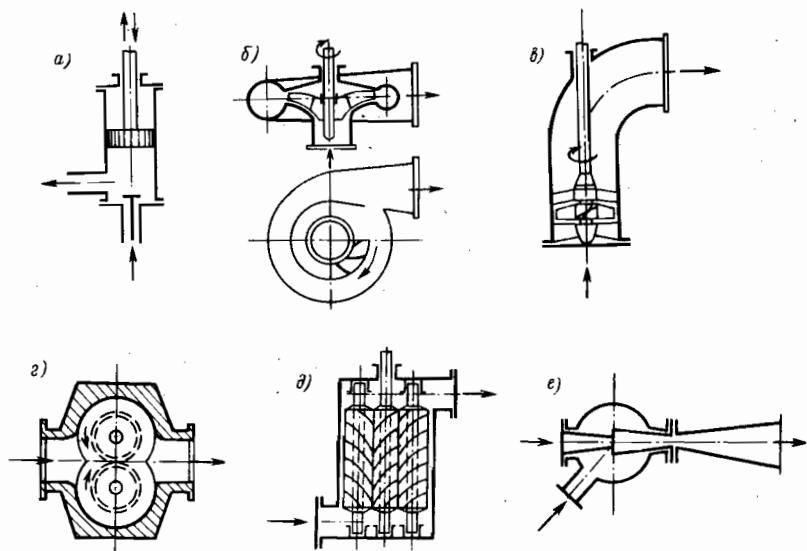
Судовые насосы (схемы): а — поршневой; б — центробежный; в — осевой; г — шестеренчатый; д — винтовой; е — струйный
